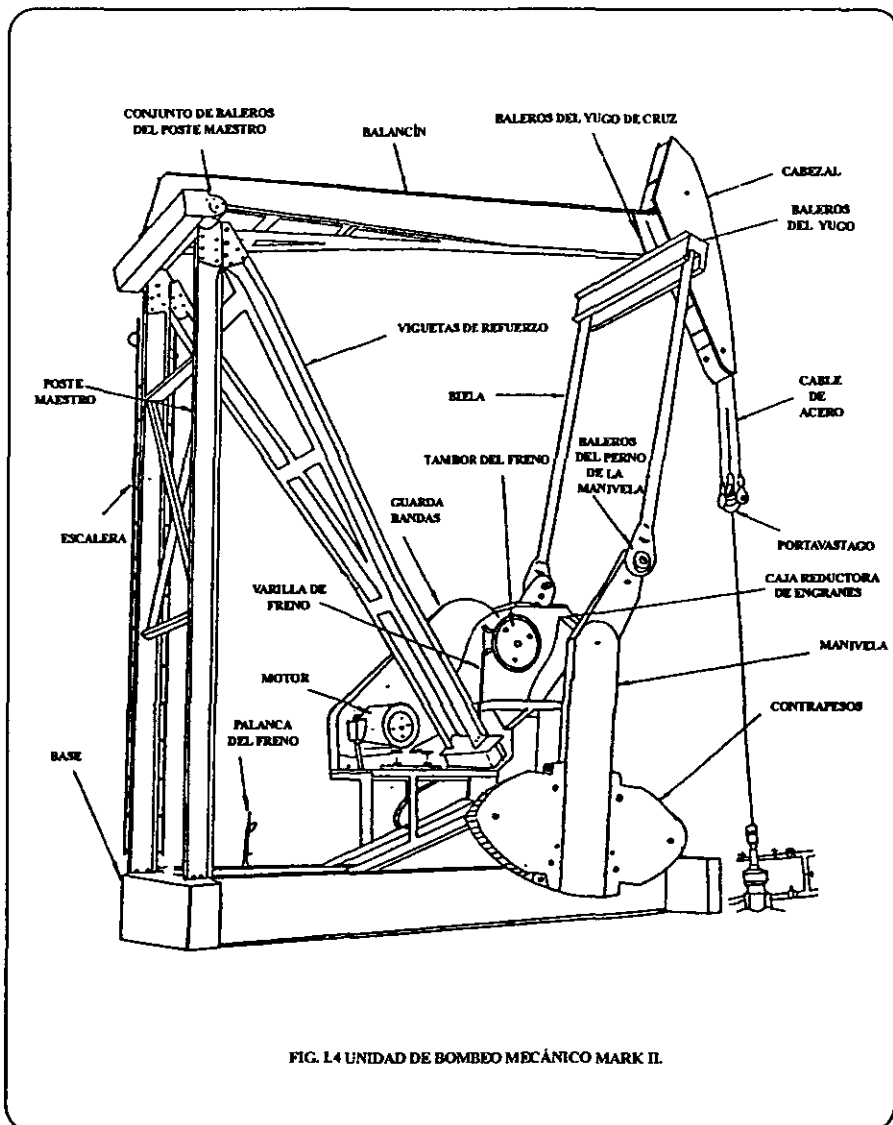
UNIDAD DE BOMBEO MECÁNICO MARK II.
